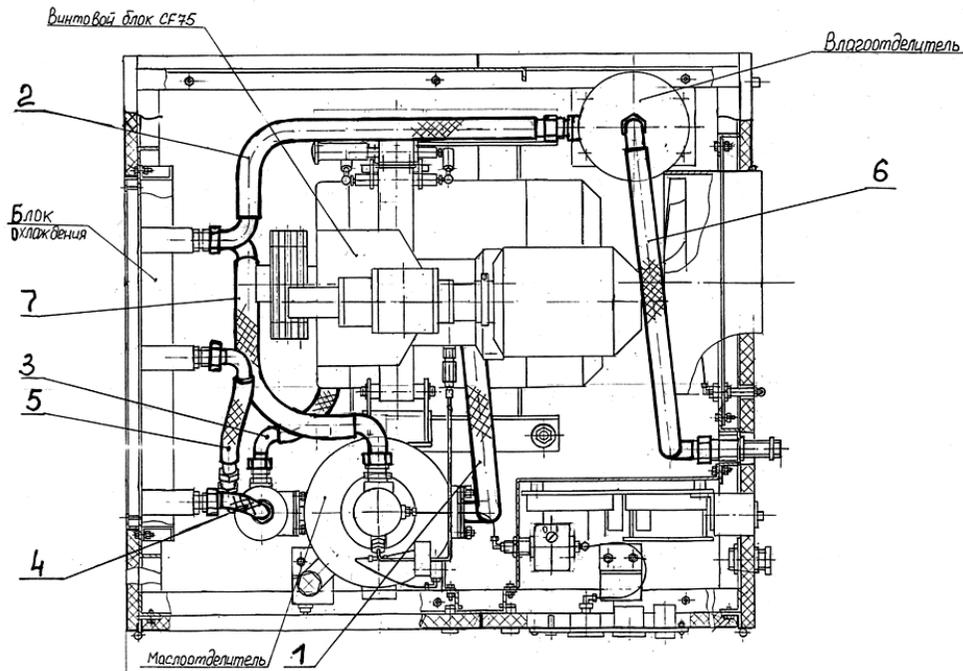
Схема расположения напорных рукавов (вид сверху)
